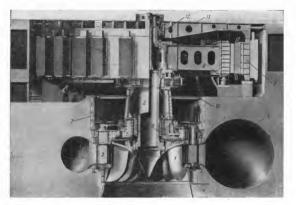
Общий вид гидроагрегата мощностью 115 тыс. көт с поворотнолопастной турбиной. 1—рабочее колесо; 2— вал турбины; 3— ваправляющий аппарат; 4— крышка турбивы; 6—вал генератора; 6— рогор генератора; 7— статор; 8— подлятики; 9— верх-
